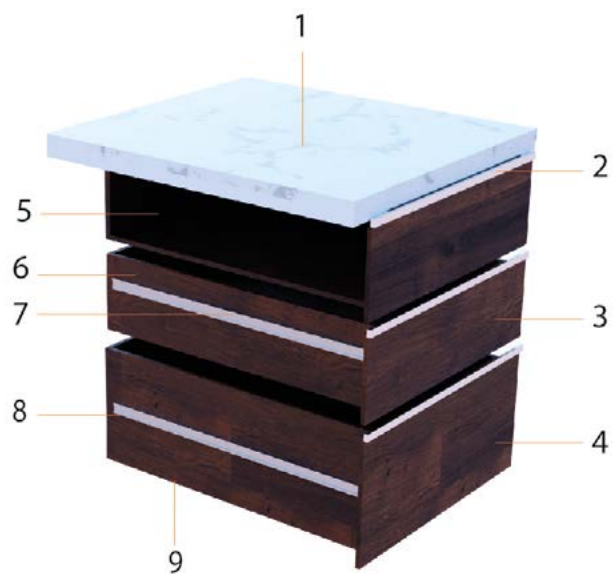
Detalle constructivo 3d cajonera con madera MDF
